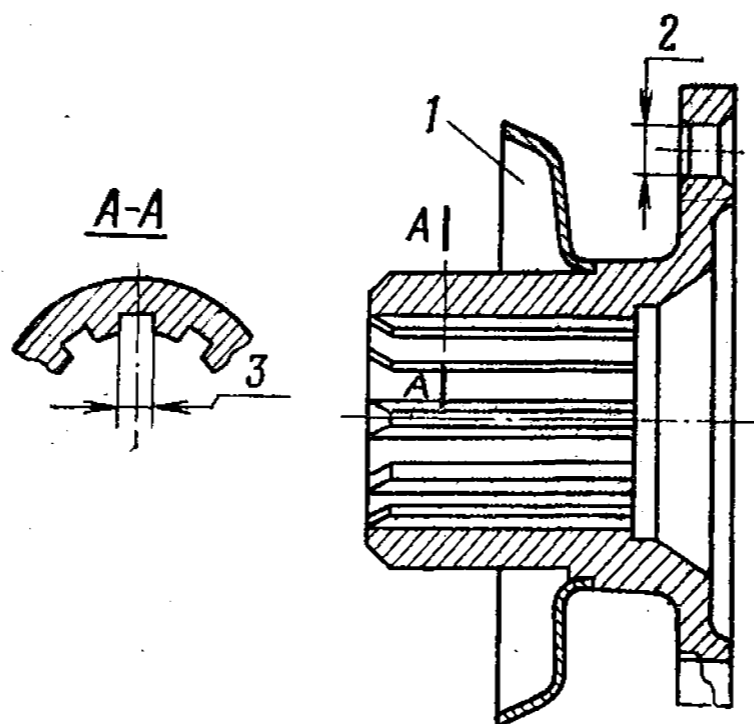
Фланец крепления промежуточного вала к валу ведущей шестерни раздаточной коробки
